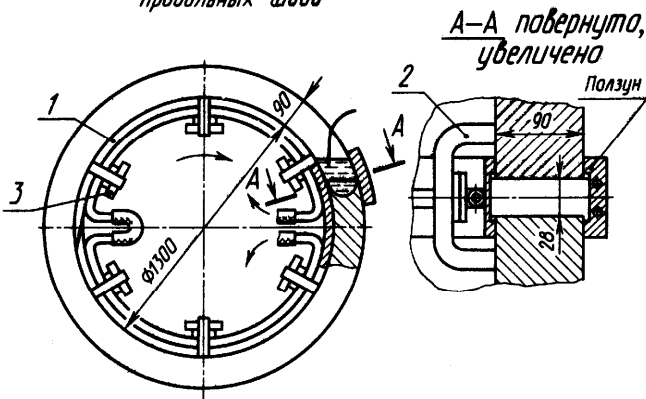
Сборка кольцевого стыка под электрошлаковую сварку
